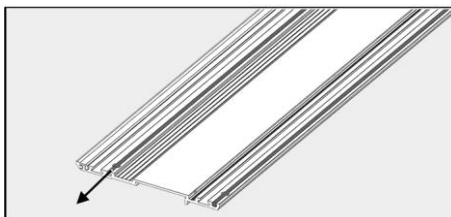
Extraer el perfil adhesivo en la parte inferior del carril guía
